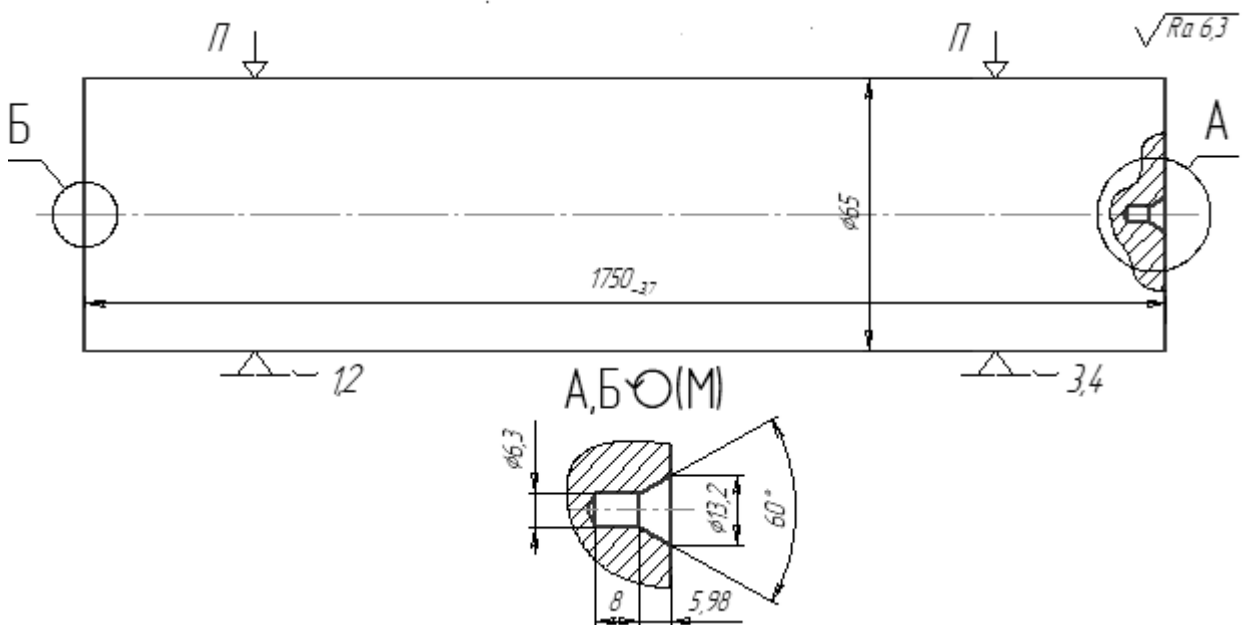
Ескіз операції 025 фрезерно-центрувальної
